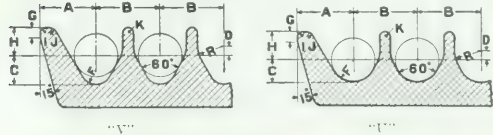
SECCIÓN TRANSVERSAL DE POLEA CON CANALES PROFUNDAS
